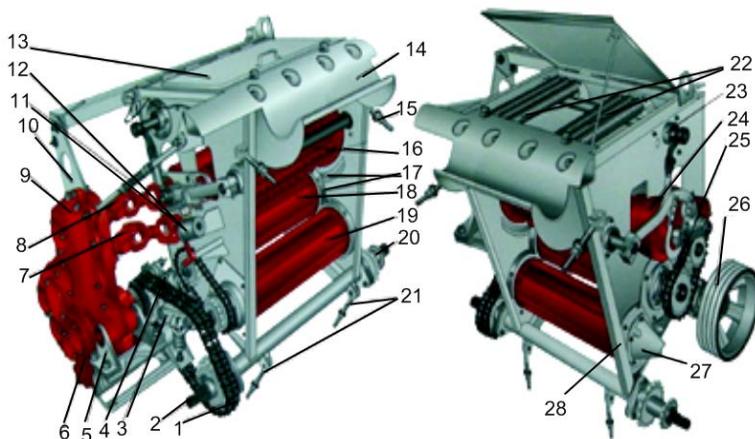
Питающий аппарат комбайна «Дон-680М»: 1 – цепь двойная привода вала контрпривода жатки; 2 – вал контрпривода жатки; 3 – рычаг натяжного устройства цепи привода жатки; 4 – рычаг включателя муфты быстрого останова; 5 – опора редуктора питателя; 6 – механизм блокировки переключения длины резки; 7 – карданный вал привода малого верхнего вальца; 8 – карданный вал привода нижнего гладкого вальца; 9 – редуктор питателя; 10 – косынка крепления редуктора; 11 – растяжка регулируемая редуктора питателя; 12 – электромагнитная муфта быстрого останова; 13 – крышка механизма подпрессовки; 14 – захват питателя; 15, 21 – стяжные болты питателя и жатки; 16 – верхний большой валец; 17 – отсекатели; 18 – валец нижний средний; 19 – валец передний нижний (с металлодетектором); 20 – блок звездочек привода жатки; 22 – блоки пружин механизма подпрессовки вальцов; 23 – вал механизма подпрессовки; 24 – редуктор верхних вальцов; 25 – цепь привода среднего нижнего вальца; 26 – шкив контрпривода питателя; 27 – место регулировки положения датчика металлодетектора; 28 – рама
